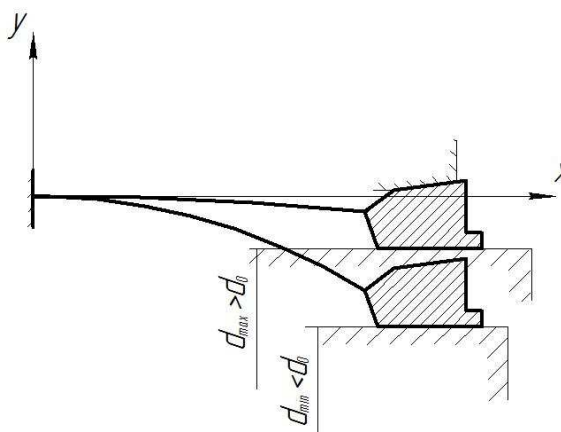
Схема контакта зажимной цанги с калиброванной заготовкой и конусом шпинделя
